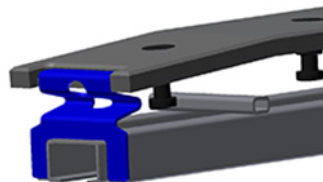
Impaktní tyč DvB 0991-001-000 [5]
